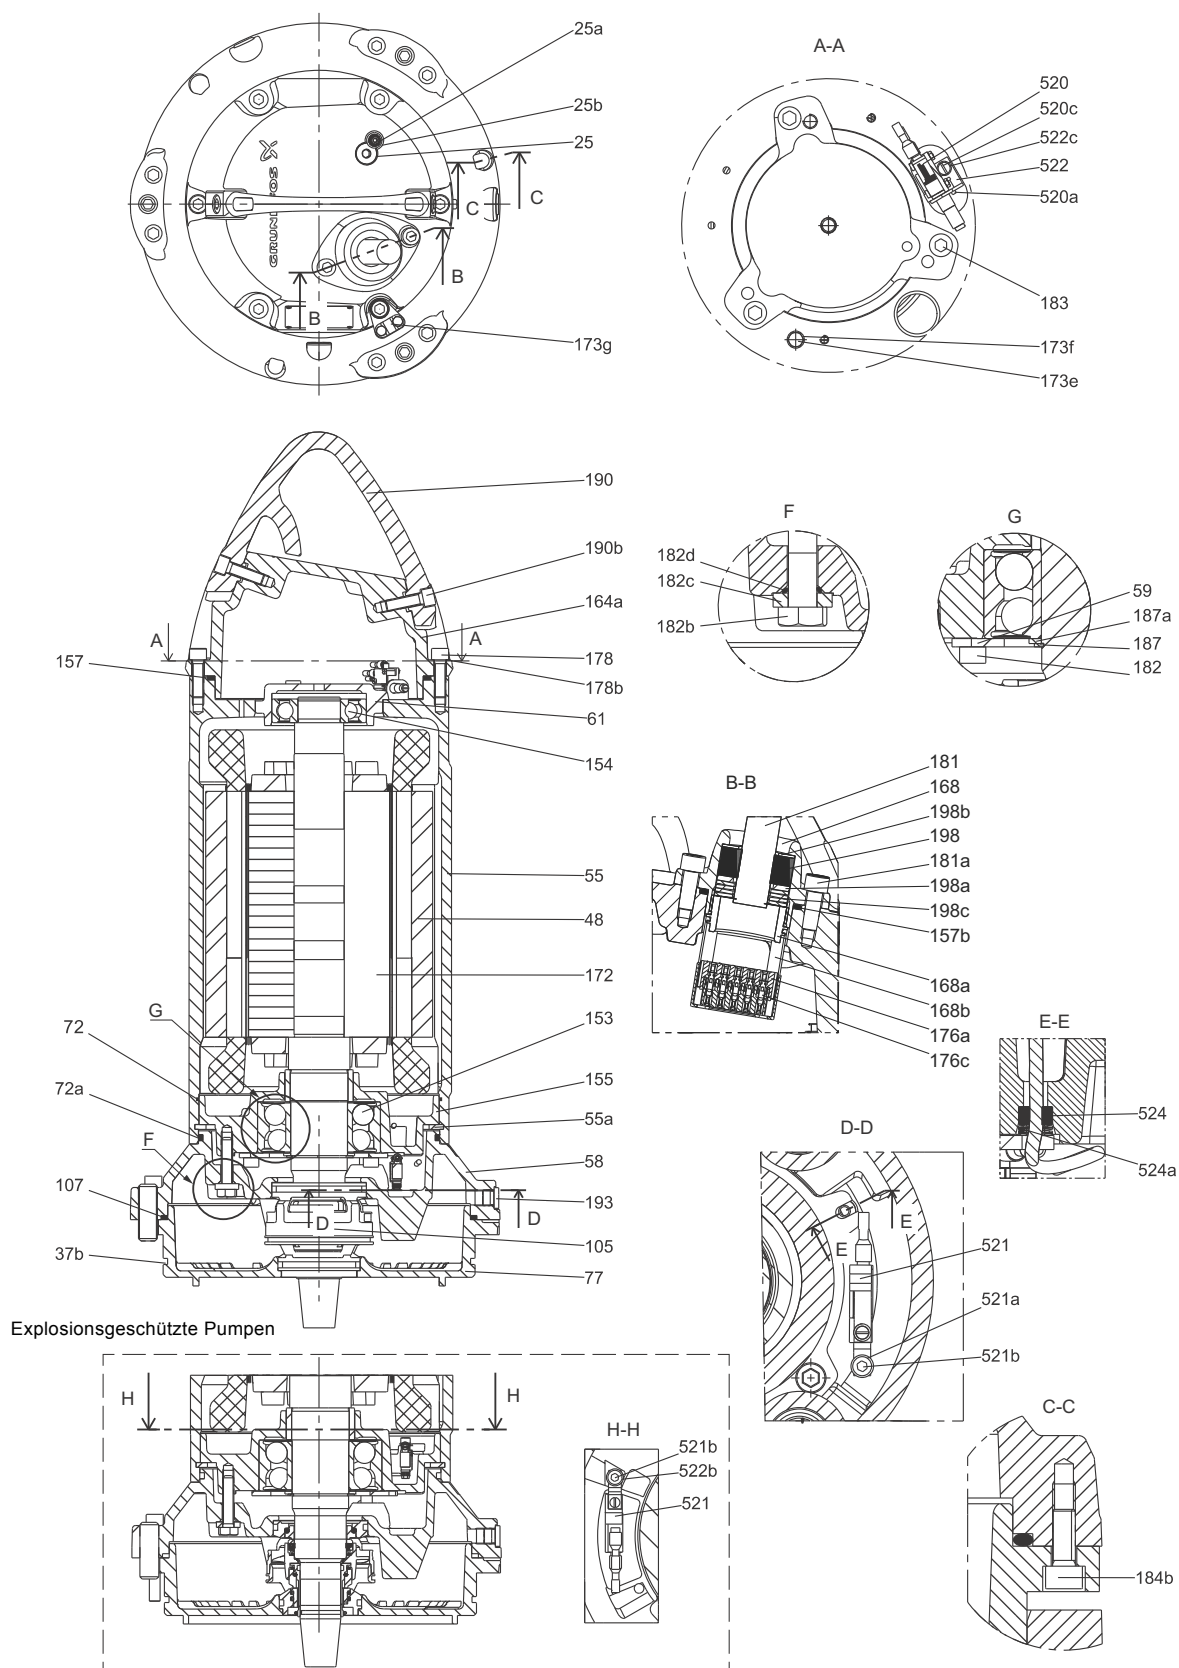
SL-Pumpen ohne Kühlmantel mit 2- und 4-poligem Motor
